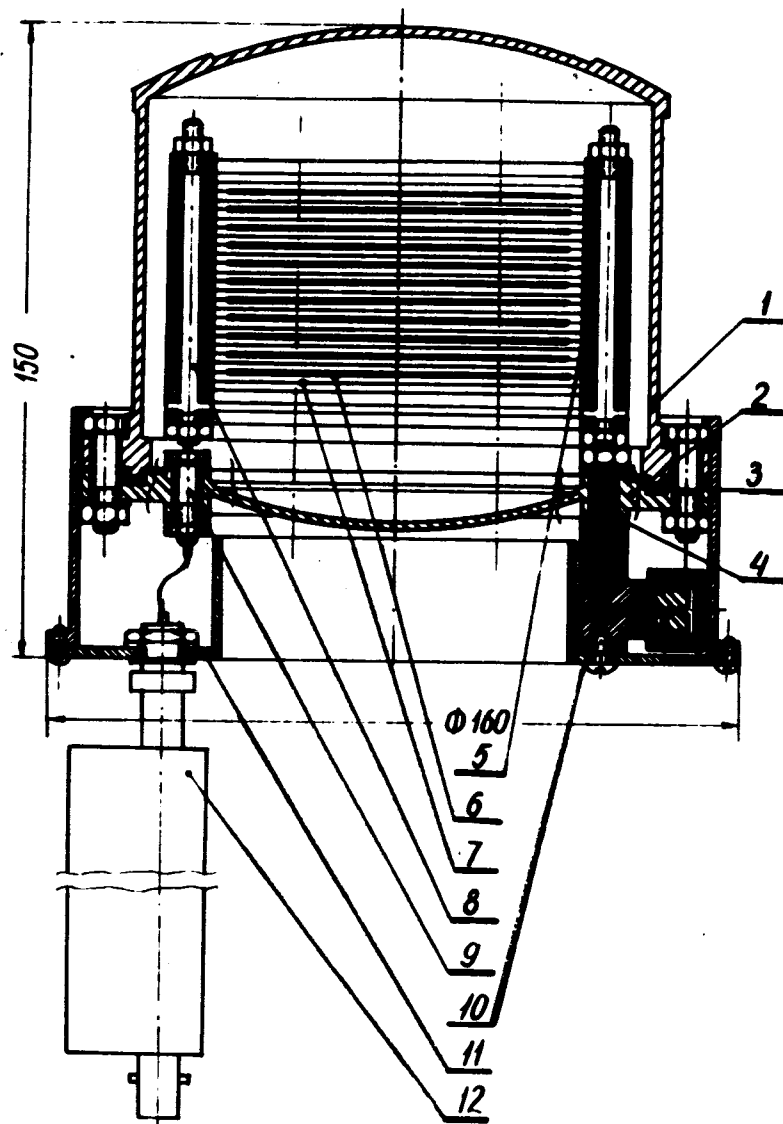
Конструкция камеры. 1 - корпус; 2 - крышка; 3 - тефлоновая прокладка; 4 - тефлоновая шайба; 5 - межэлектродное тефлоновое кольцо; 6 - алюминиевая подложка с ^{235}U ; 7 - чистый алюминиевый электрод; 8 - разборный латунный каркас; 9 - латунный электродный вывод; 10 - латунный вентиль; 11 - электрический алюминиевый экран; 12 - дюралюминиевая коробка усилителя.
